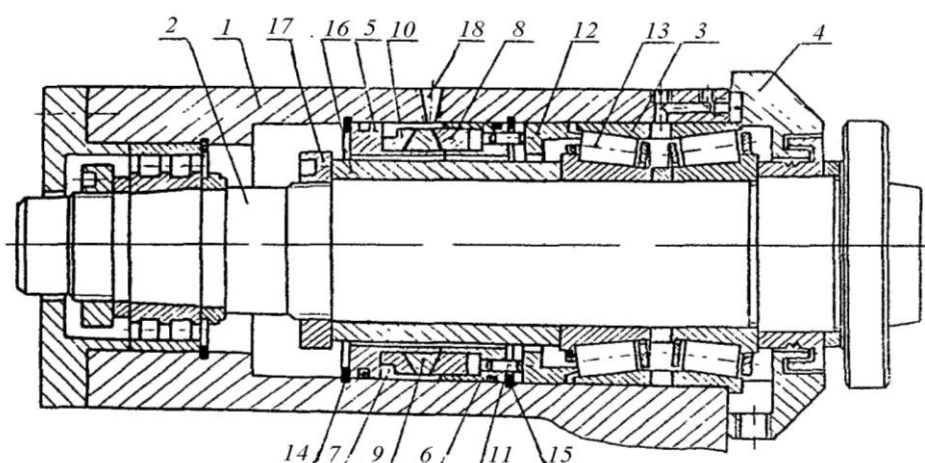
Конструкция шпиндельного узла на роликовом подшипнике
